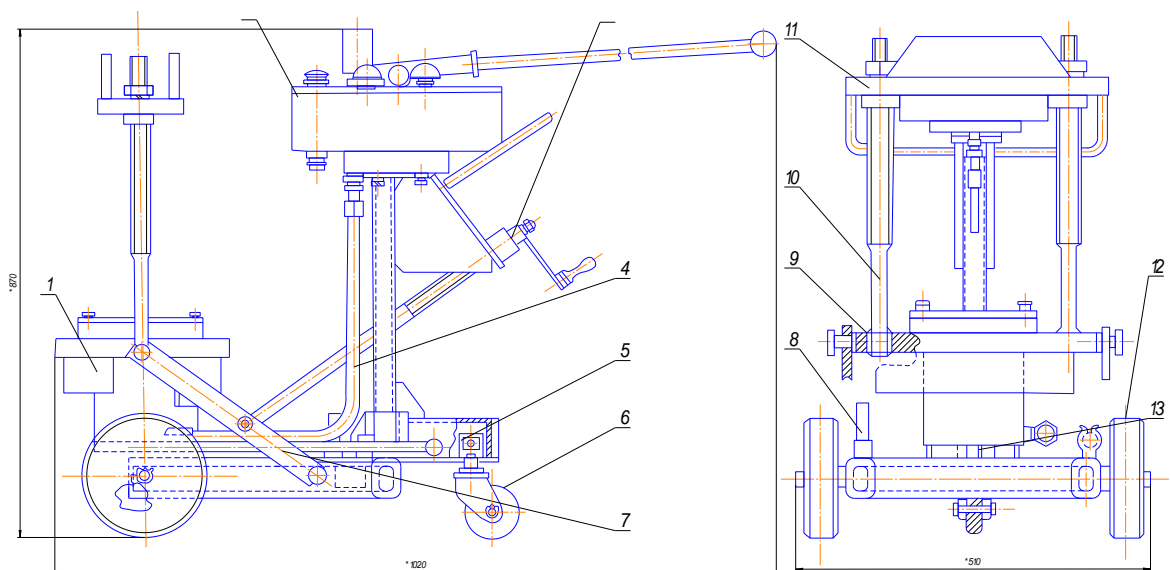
Конструкція пристрою для випресовування шворнів
